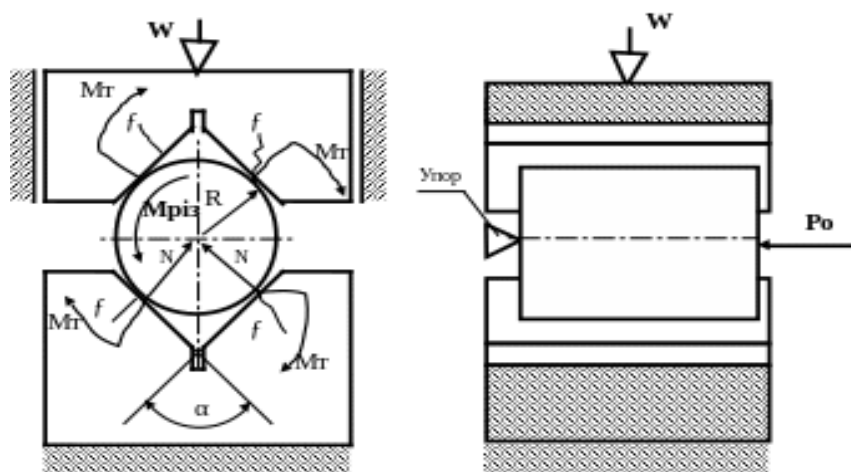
Схема затиску заготовки у двох призмах з упором
